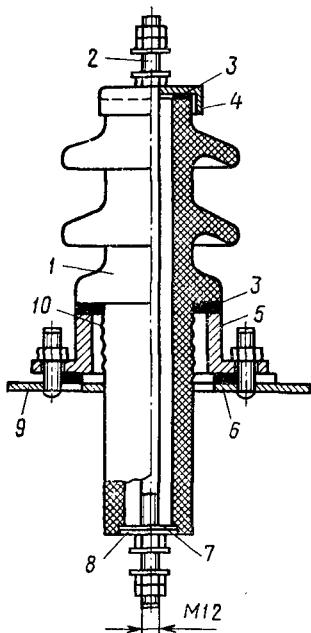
Схема армированного ввода напряжением 6–10 кВ наружной установки:
